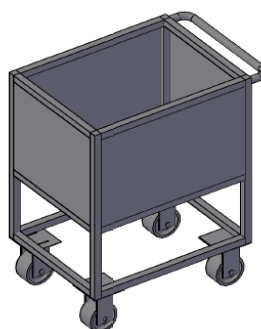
DISEÑO DEL CARRO PARA ALMACENAR DEDOS DE LA PARRILLA
